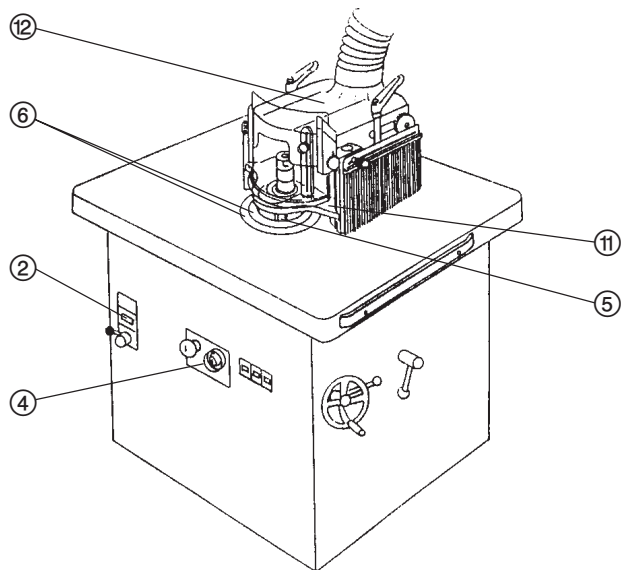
Einspindelige senkrechte Tischfräsmaschine ausgerüstet zum Bogenfräsen
